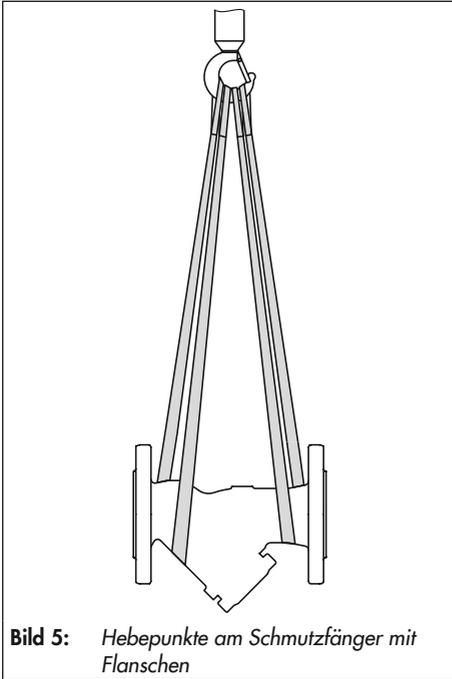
Hebepunkte am Schmutzfänger mit Flanschen
